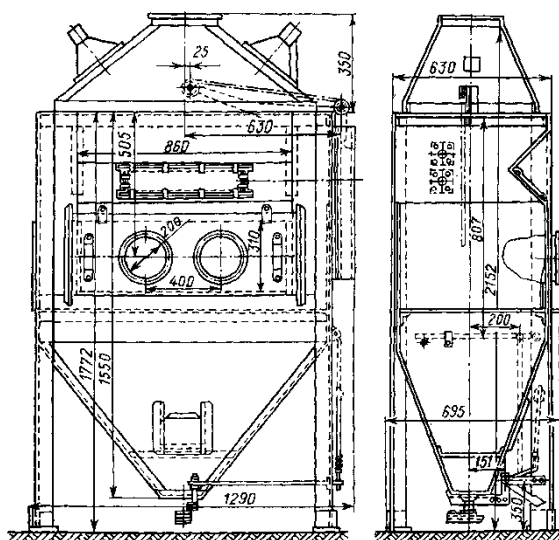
Установка для піскоструминної обробки деталей
